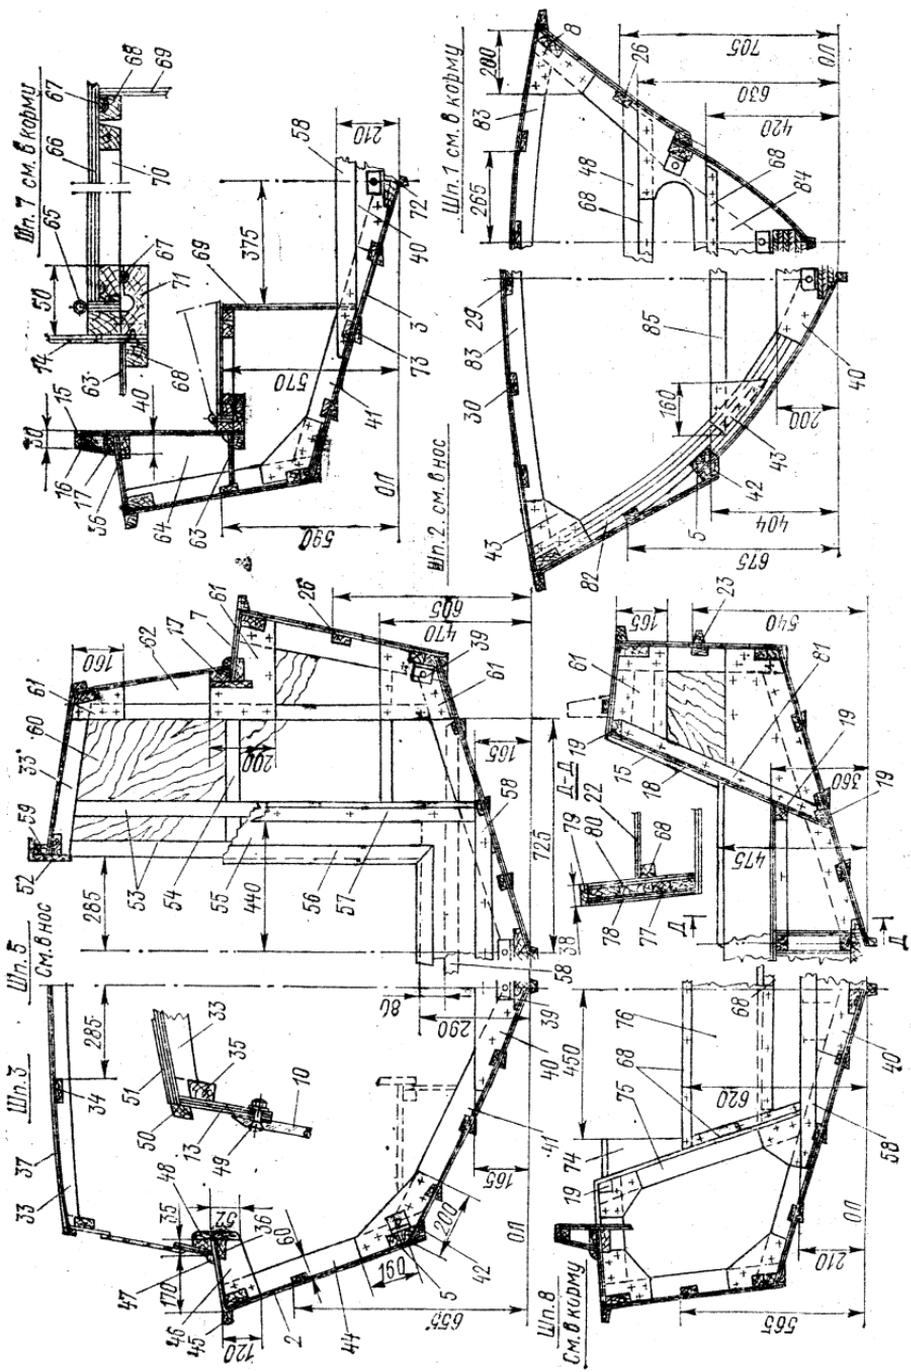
, а. Конструктивный продольный разрез, набор днища и палубы (см. стр. 327) и поперечные сечения.
